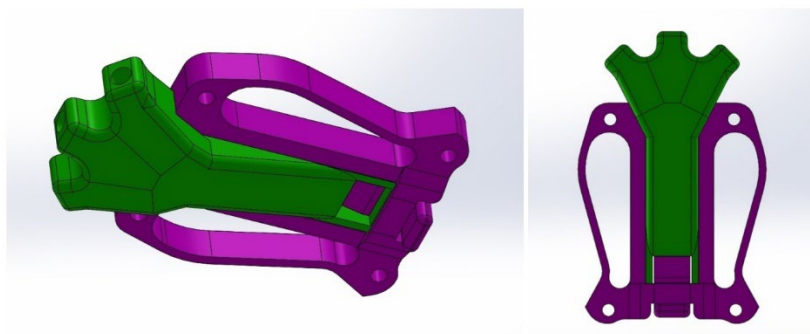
Vista en detalle del anclaje de las protecciones en 3D.
